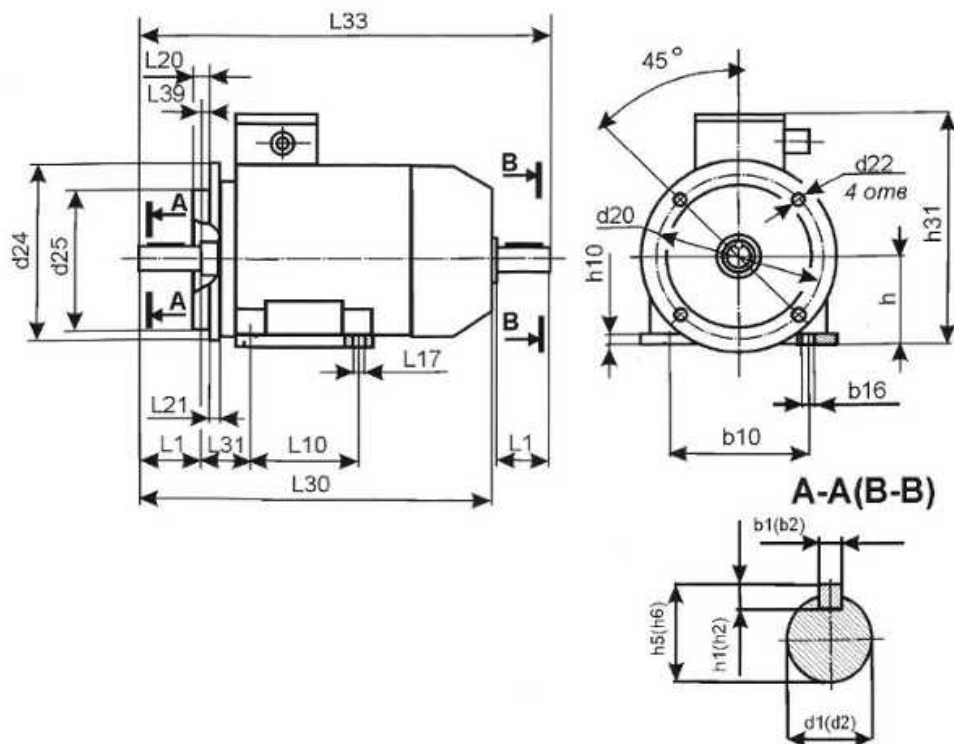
Габаритно-установочные и присоединительные размеры двигателя АИР56АУЗ
